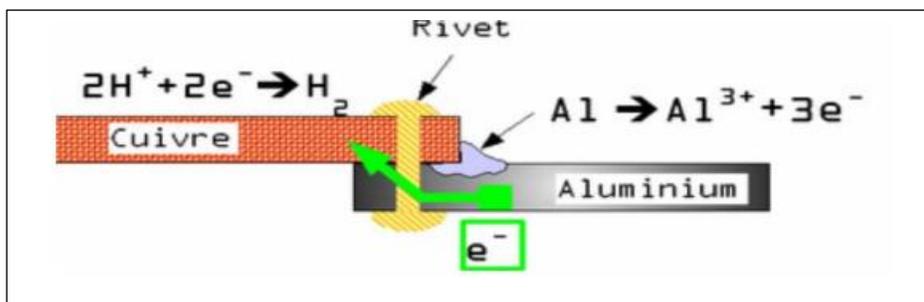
Assemblage de tôles d'aluminium et de cuivre
